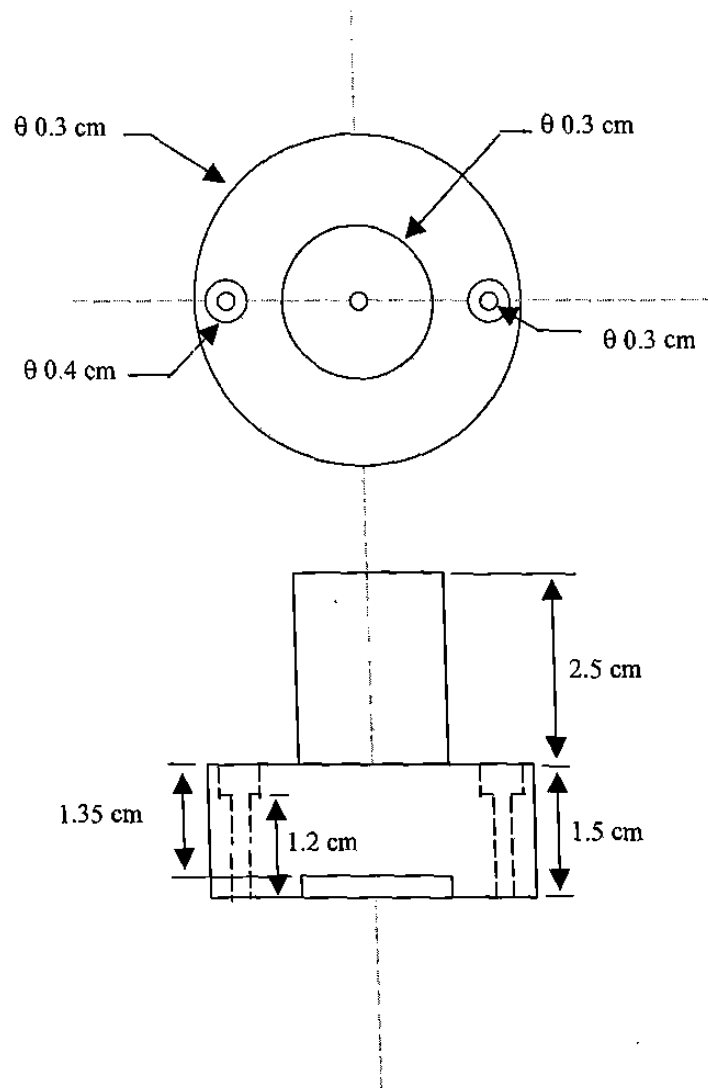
Dimensiones del herramental que fue elaborado para la realización de los ensayos mecánicos
